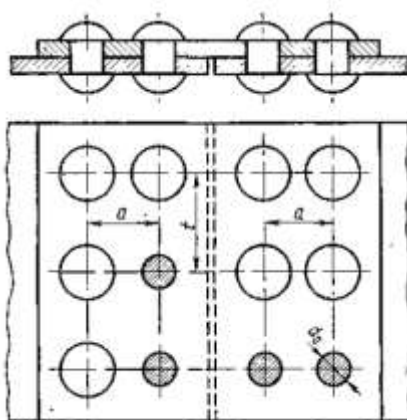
Двурядный односрезный параллельный заклепочный шов с одной накладкой
